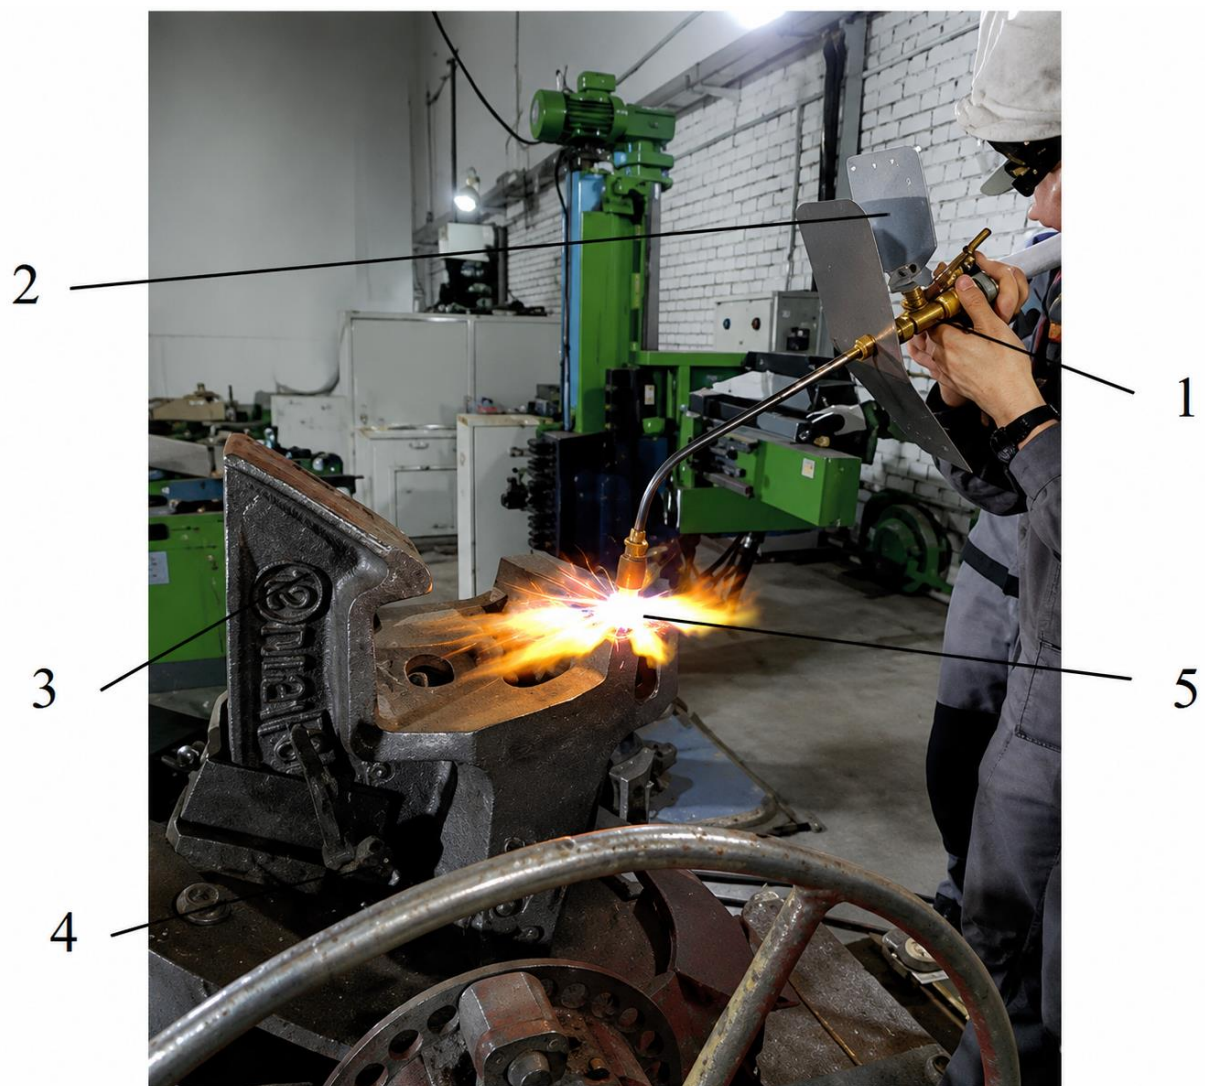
Встановлення плазово-порошкового наплавлення
